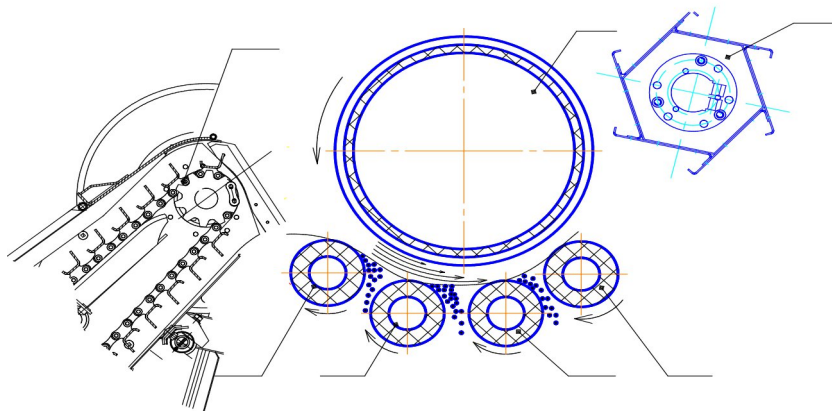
Схема молотильного пристрою з еластичною рифленою робочою поверхнею
